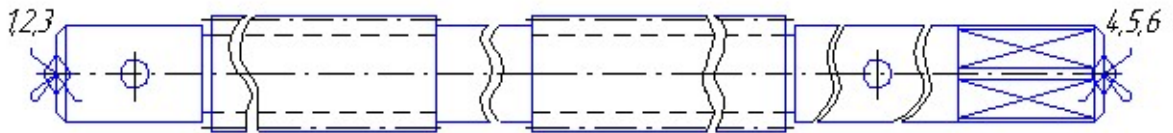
Вибір баз при свердлуванні отворів та фрезеруванні лисок
